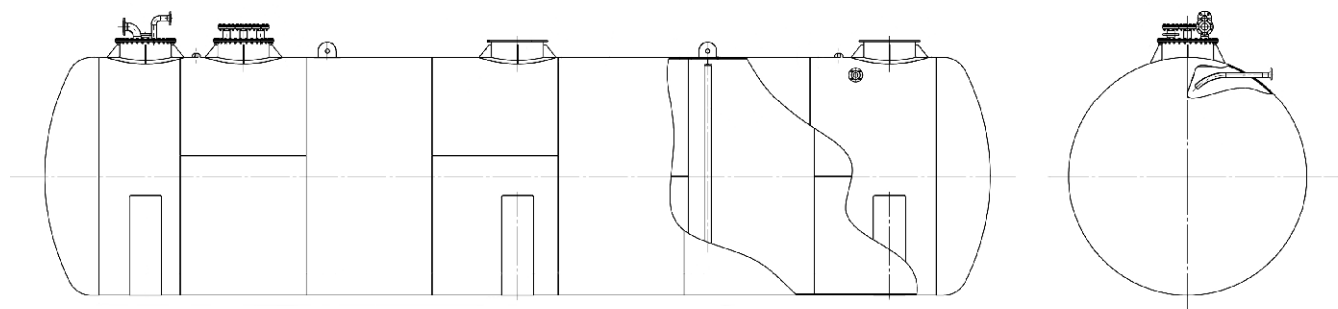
Общий вид эскиза резервуара РГС-63
